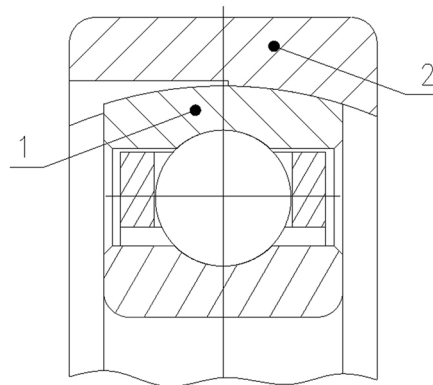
Конструкция опоры с защитой от несоосности статора и ротора
